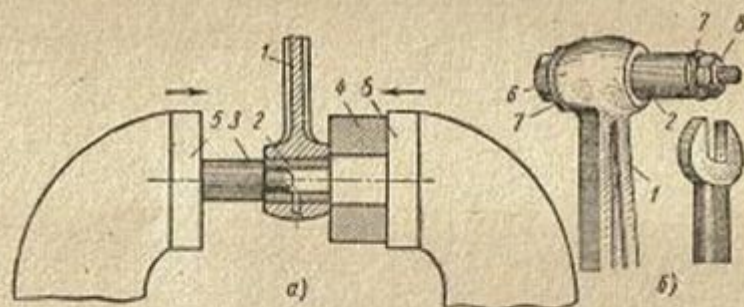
Запрессовка и выпрессовка втулки верхней головки шатуна:
